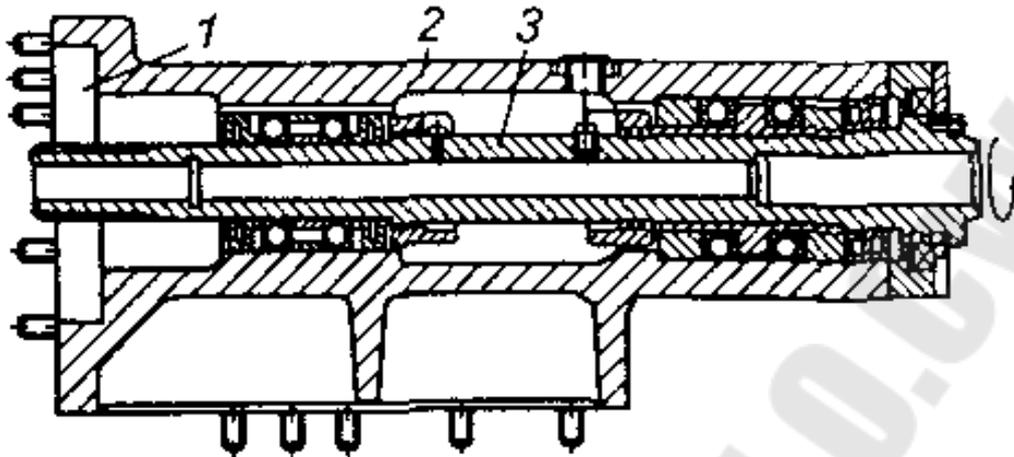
Конструкция расточной бабки агрегатного станка
